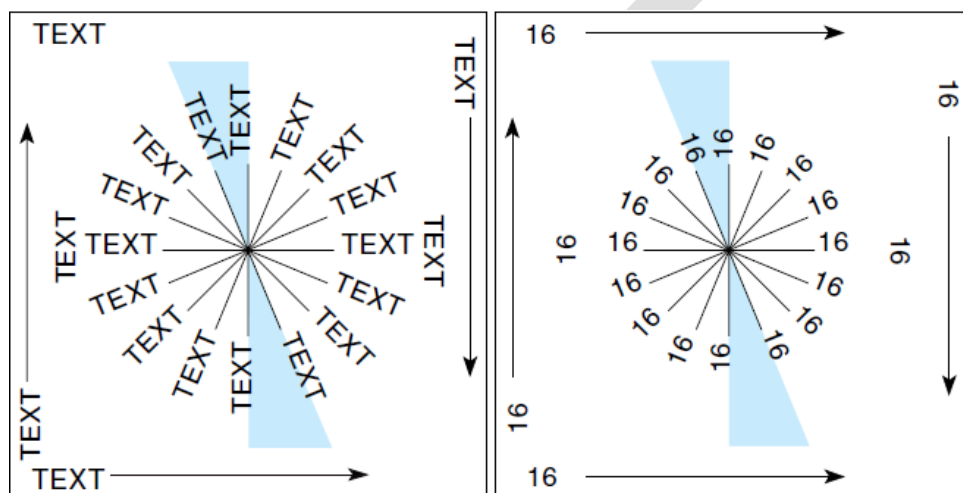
Placering av text i förhållande till punkt- och ytformade element.
